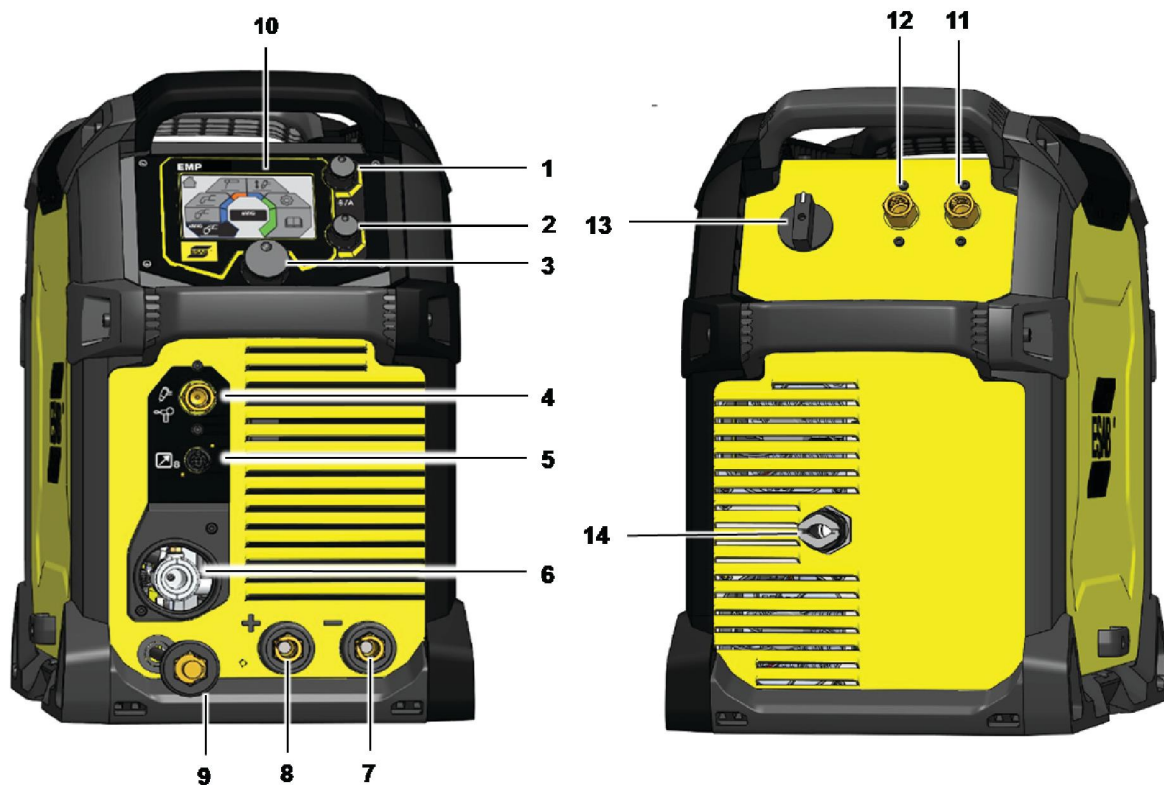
Vues avant et arrière : Modèle EMP 285ic
